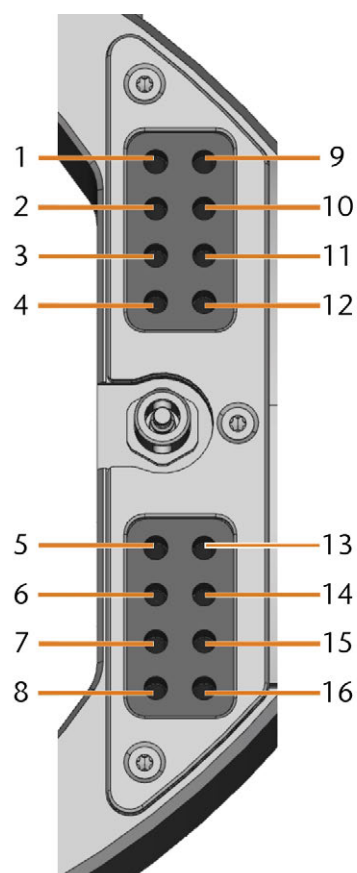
WERKZEUGE IN DIE WERKZEUGPOSITIONEN EINSETZEN
